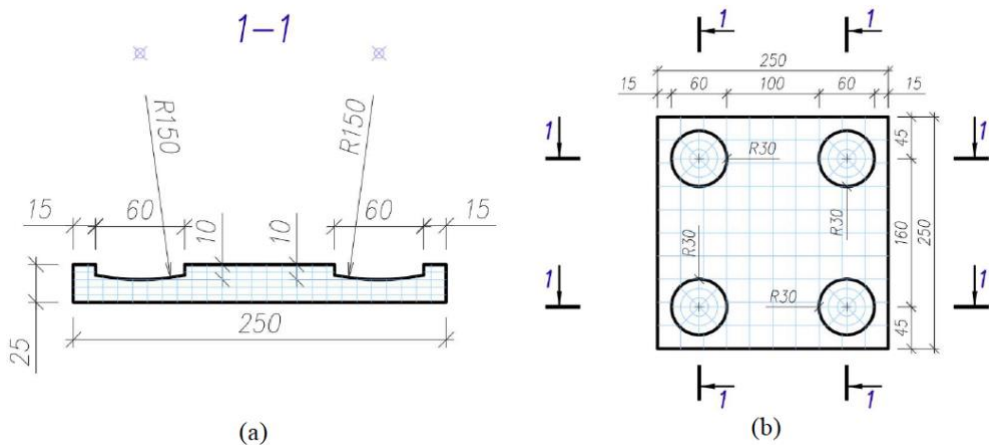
Figura XI.- (a) Vista de sección y (b) Vista en planta del espécimen de la superficie cóncava, unidades en milímetros.
